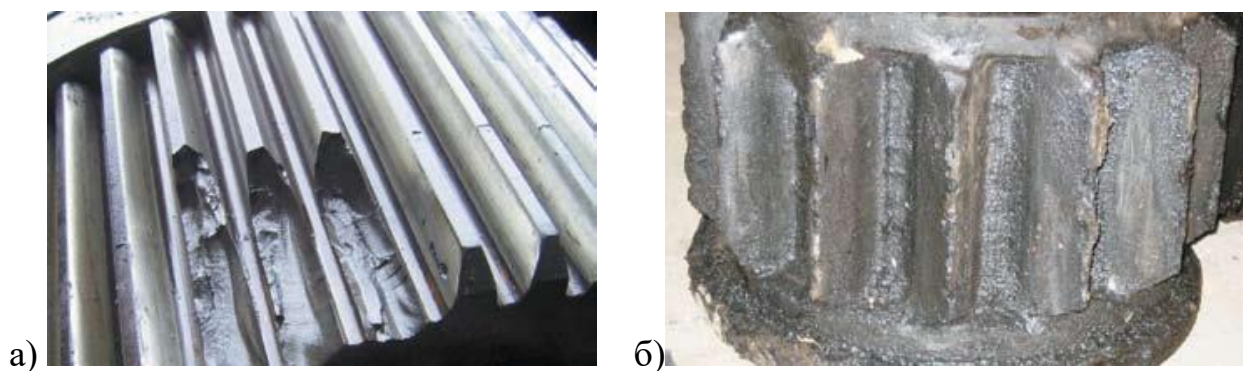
Дефекты зубчатых колес и шестерен: а) излом зубьев из-за воздействия динамических ударов; б) абразивный износ
